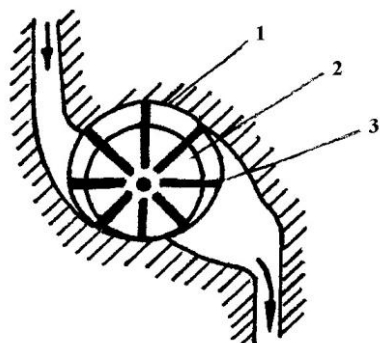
г. Шиберный насос: 1 – корпус; 2 – ротор; 3 - пластина
